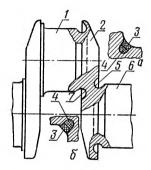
Подготовка трещины на шейках коленчатого вала двигателя ЗИЛ-164 под заварку:
